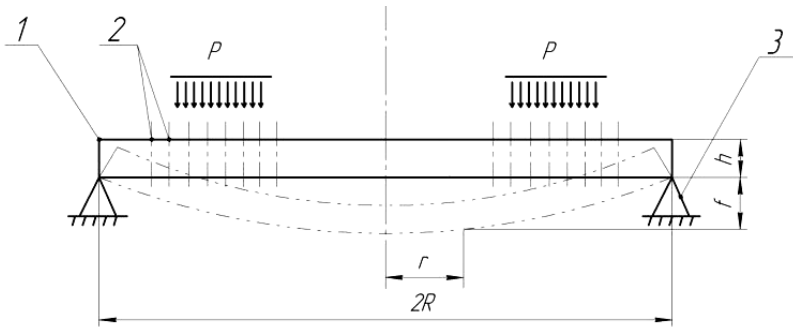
Схема деформаций корпуса сплошной матрицы с шарнирным закреплением по наружному контуру:
